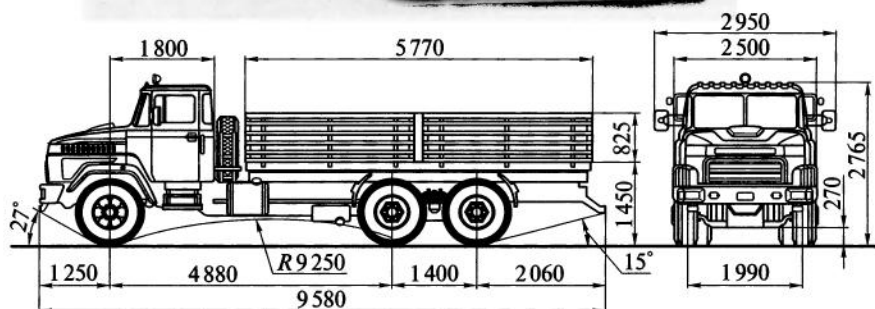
Бортовой автомобиль КрАЗ-65053
